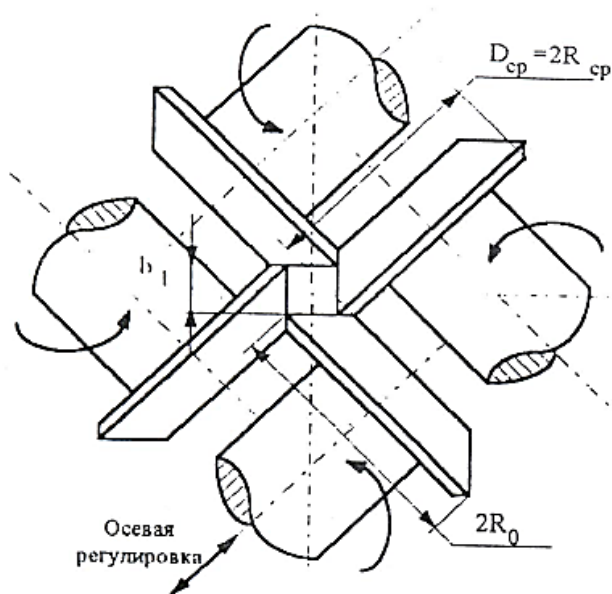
Схема валкового узла четырехвалковой калибровочной клетки
